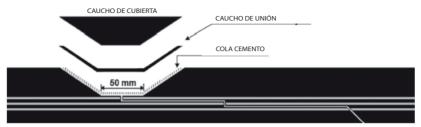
Aplicación del adhesivo cemento y caucho de unión
